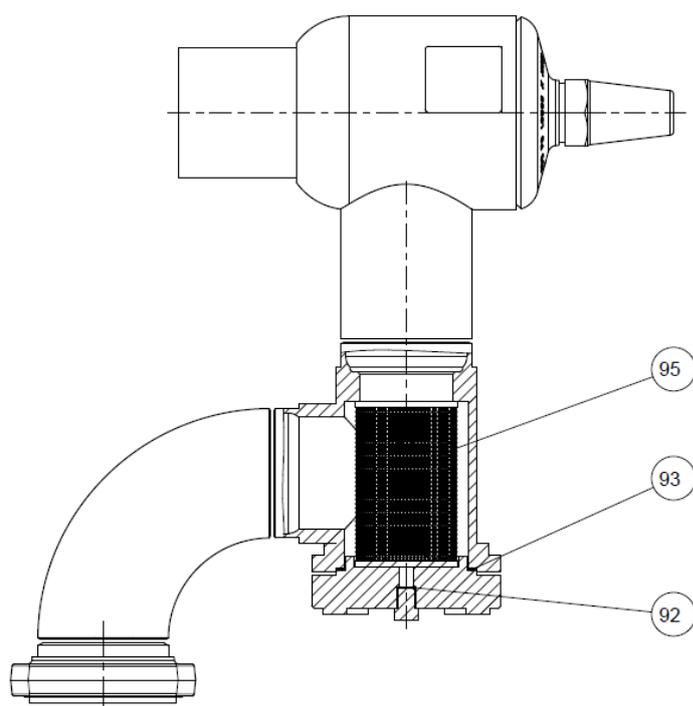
Детальный чертеж входного фильтра KS 80-P
